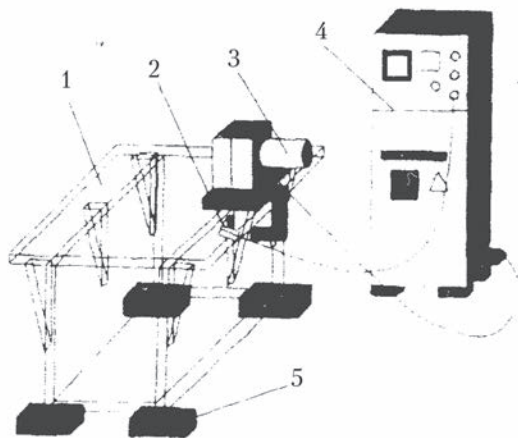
Схема вибрационной обработки сварных конструкций
